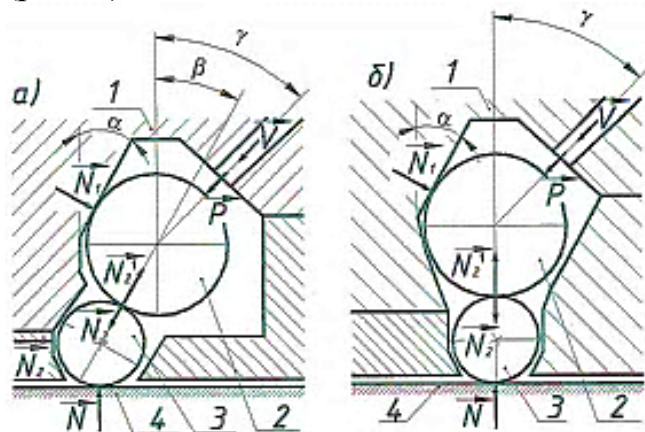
Принципиальные схемы воздействия сил на шары инструмента и обрабатываемую поверхность: а – случай А, $\beta \neq 0$; б – случай В, $\beta = 0$; 1 – направляющая поверхность; 2 – шар-ударник; 3 – шар-боек; 4 – обрабатываемая поверхность
